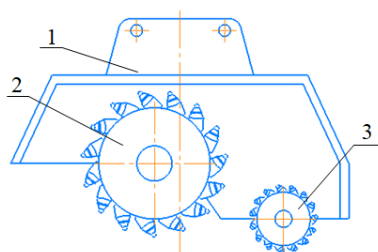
Схема навесной фрезы с двумя фрезерными барабанами:
